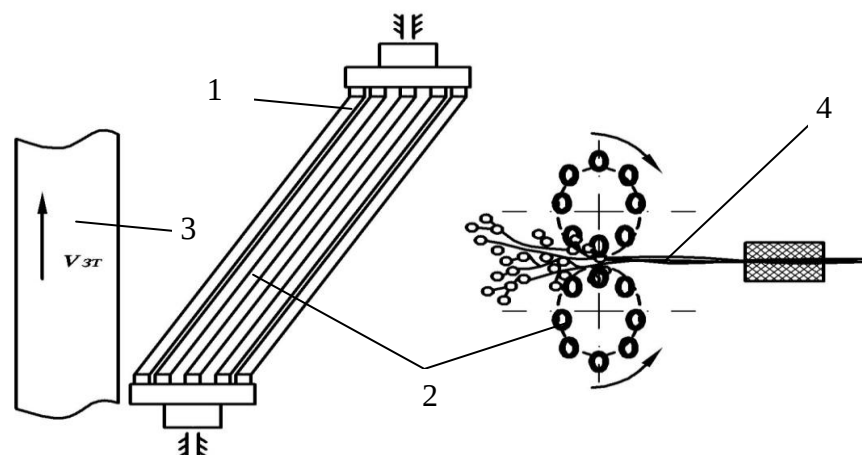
Апарат роторно-планчатого типу: 1 – барабан; 2 – планка;
